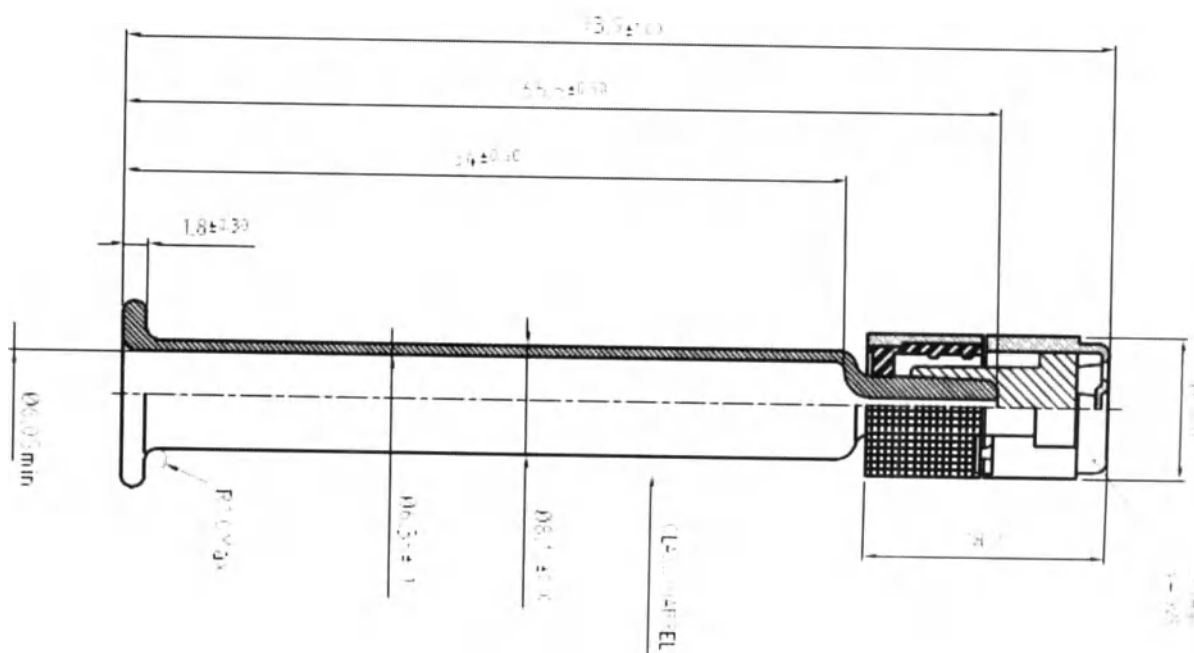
Конструкция цилиндра шприца с Luer Lock
